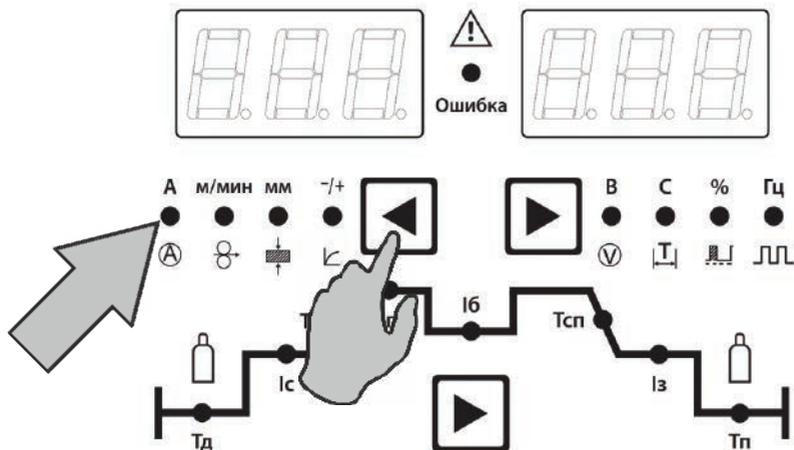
Установка основного сварочного тока.
